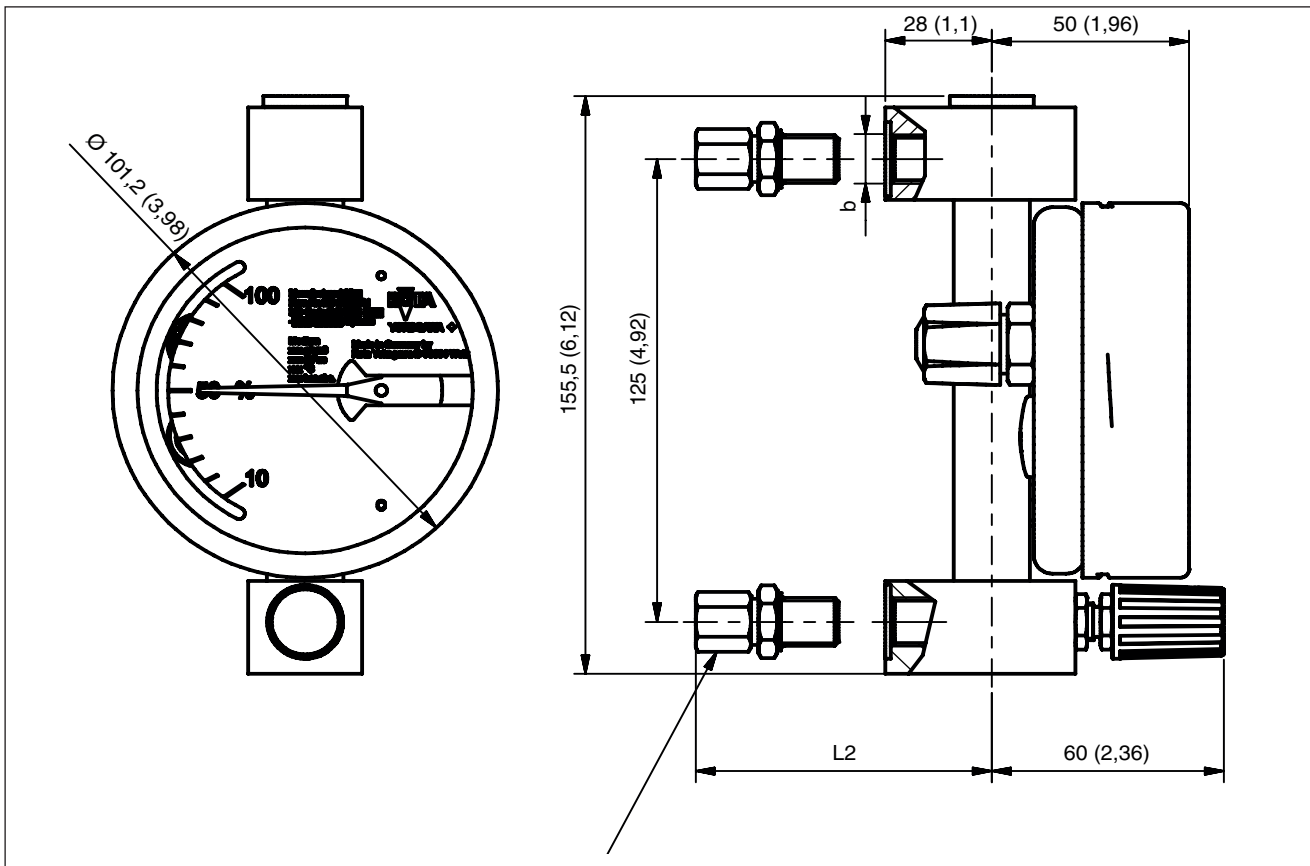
Ausführung mit Ventil im Eingang, Abmessungen in mm (Zoll)
